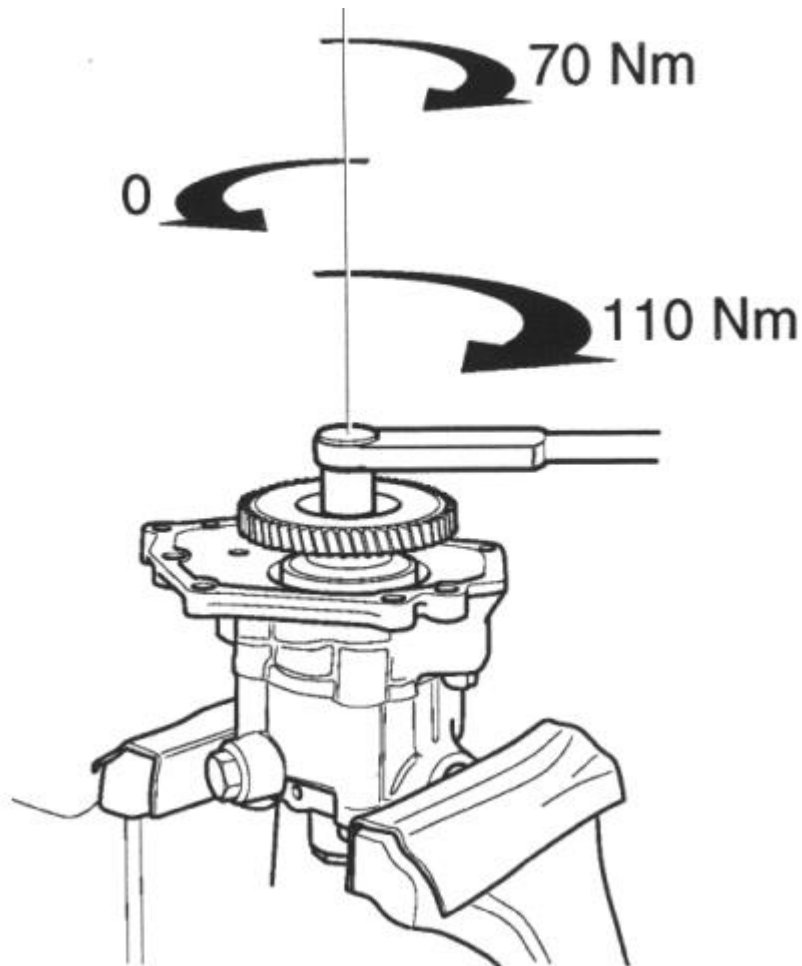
Порядок та зусилля закручування гайки шестерні
